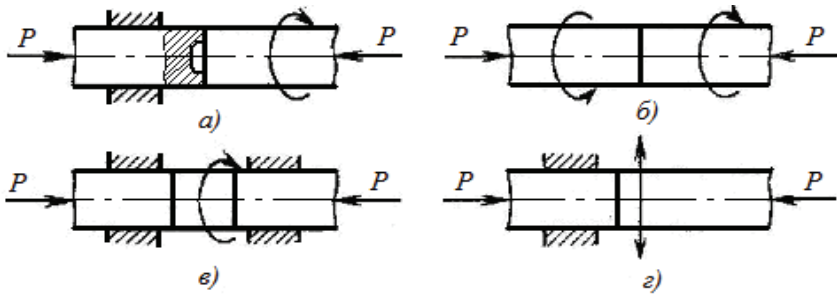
Принципиальные схемы сварки трением: а — вращение одной детали; б — вращение обеих деталей; в-сварка неподвижных деталей с вращающейся вставкой; г — сварка при возвратно-поступательном движении одной детали
